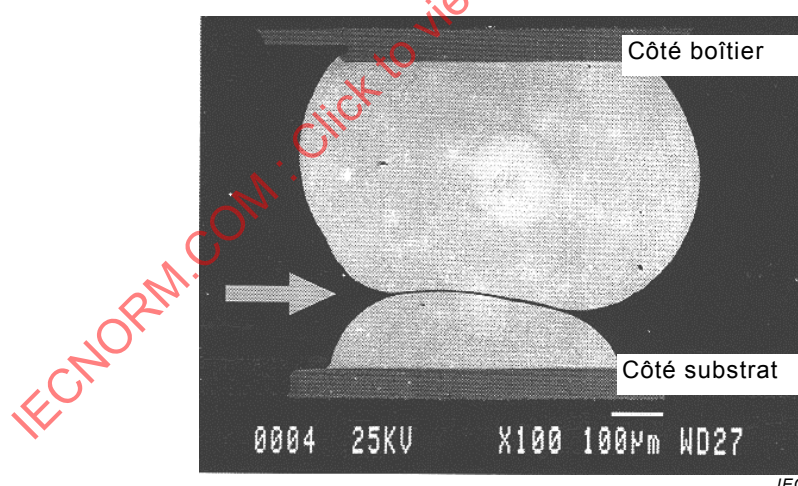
Soudure repoussée par contamination sur la surface de la boule de soudure
